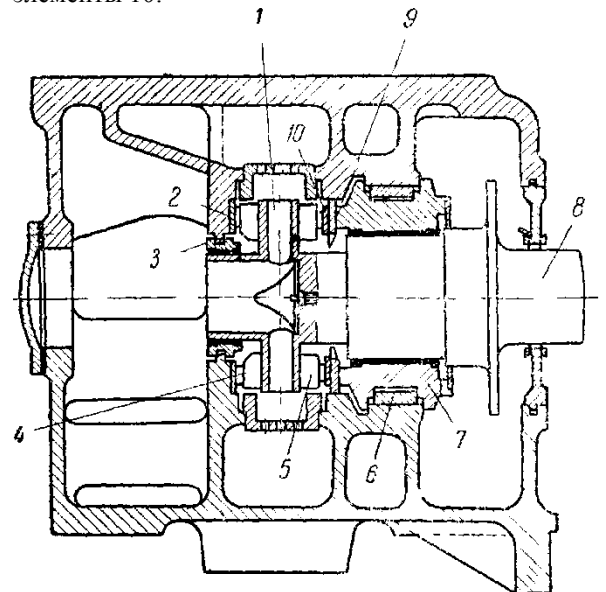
Опорно-упорный подшипник турбины КТЗ. 1—упорный диск—колесо масляного насоса, 2—регулирующие кольца, 3—уплотнение, 4—установочный сегмент, 5—рабочий сегмент, 6—опорная подушка, 7—вкладыш опорного подшипника, 8—вал турбины, 9—установочные кольца, 10—упругие элементы.
